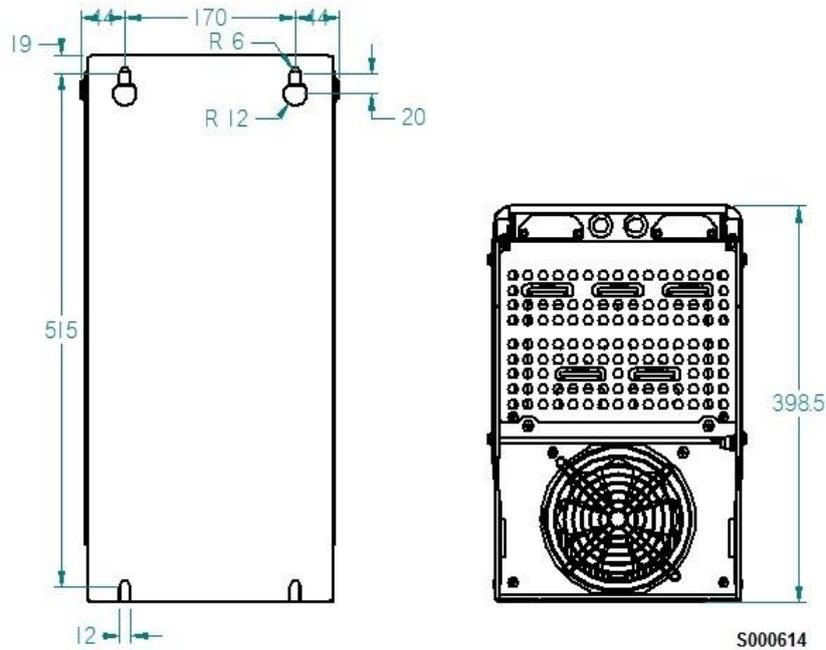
Dimensioni e punti di fissaggio dell'AC/DC UNIT 465
